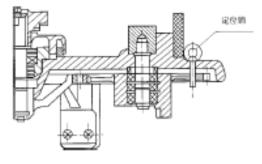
Chaveta de Seguridad de Posición Montaje del Ruptor
